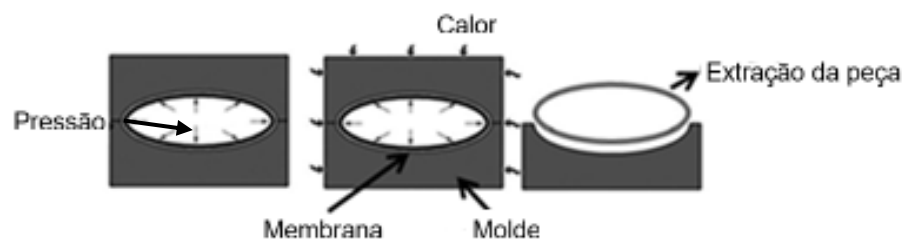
Processo de moldagem com manga insuflável (adaptado de [41])
